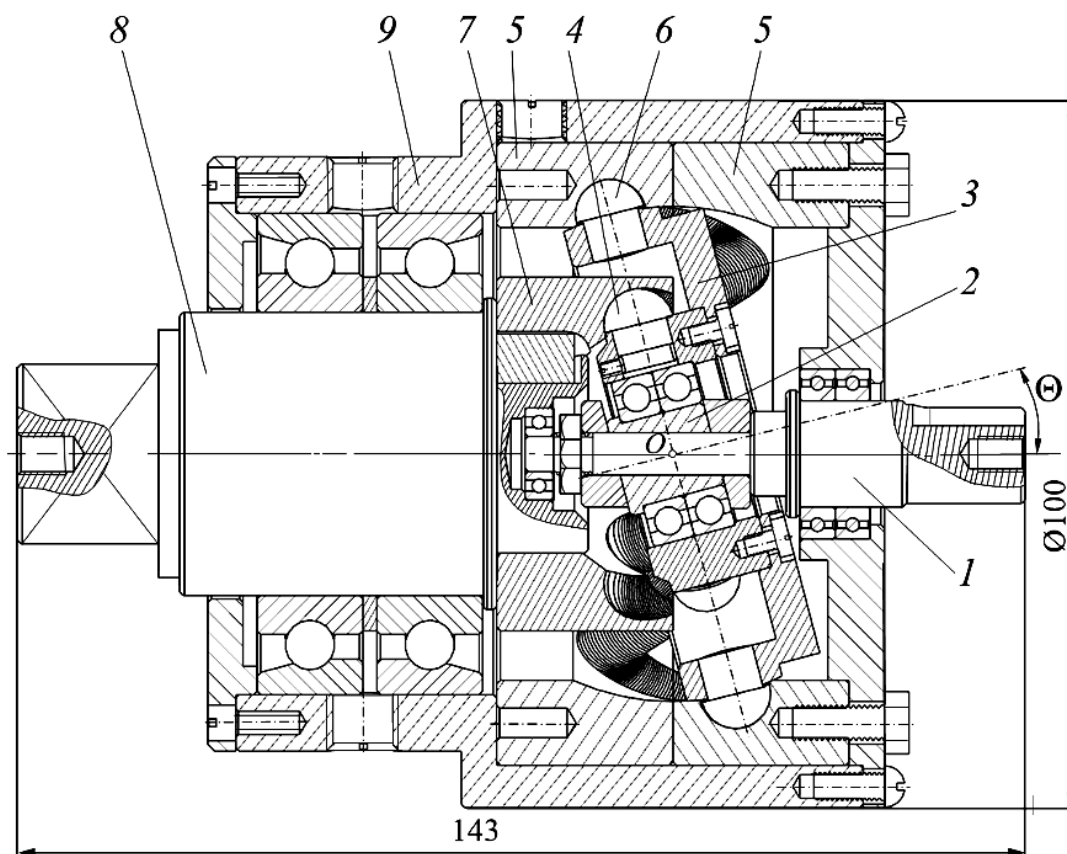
Общий вид редуктора с СРП с двухрядным сателлитом: 1 – ведущий вал; 2 – эксцентрик; 3 – составной сателлит; 4 – ролики внутреннего ряда; 5 – остановленные кулачки; 6 – ролики наружного ряда; 7 – ведомый кулачок; 8 – ведомый вал; 9 – корпус
